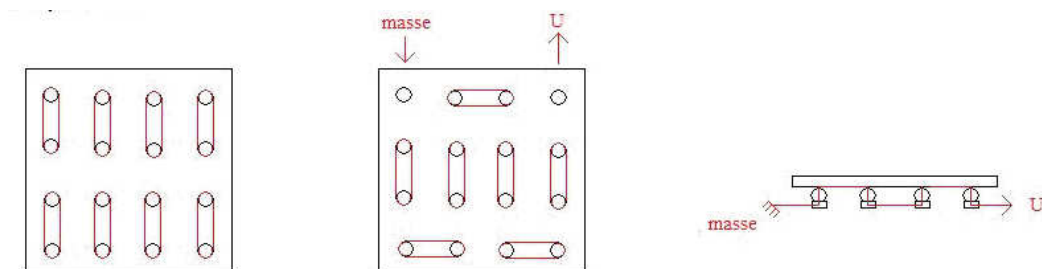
Exemple de chaîne électrique – a) Billes reliées par des pistes d'aluminium sur la puce – Au milieu, plot de cuivre sur le circuit imprimé – b) Vue en coupe du composant assemblé sur circuit imprimé, et représentation schématique du passage du courant électrique
